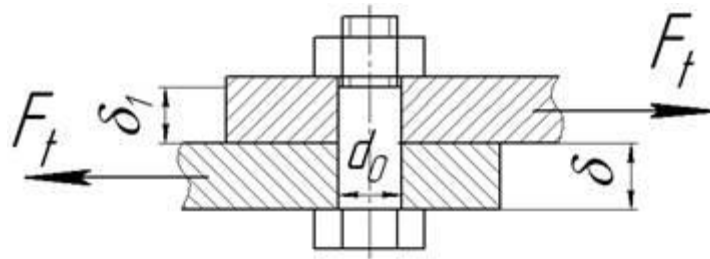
Схема нарізного з'єднання чистовим болтом
